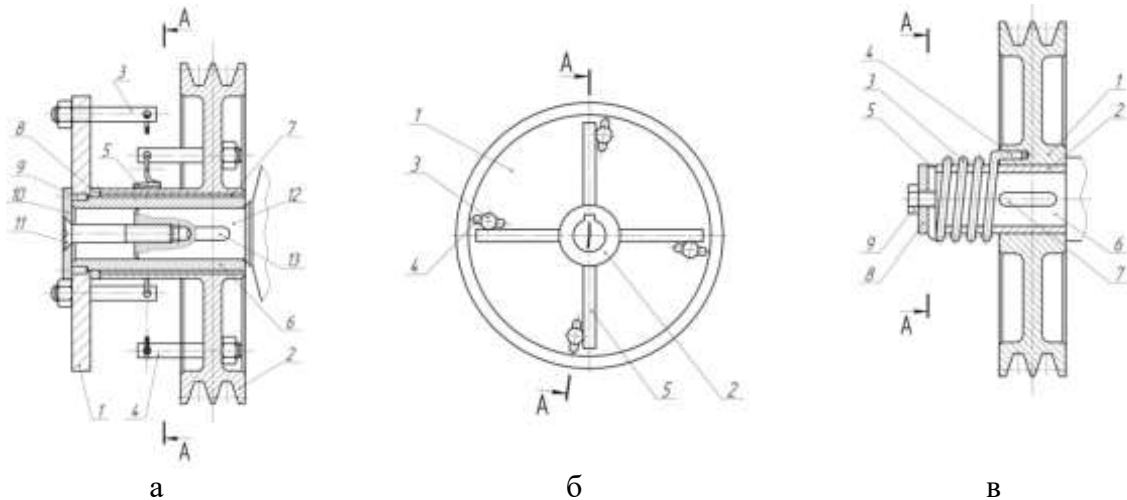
Нові конструкції пружних муфт: а – з циліндричними пружинами розтягу; б – з консольними плоскими пластинчастими пружинами; в – з циліндричною пружиною кручення
